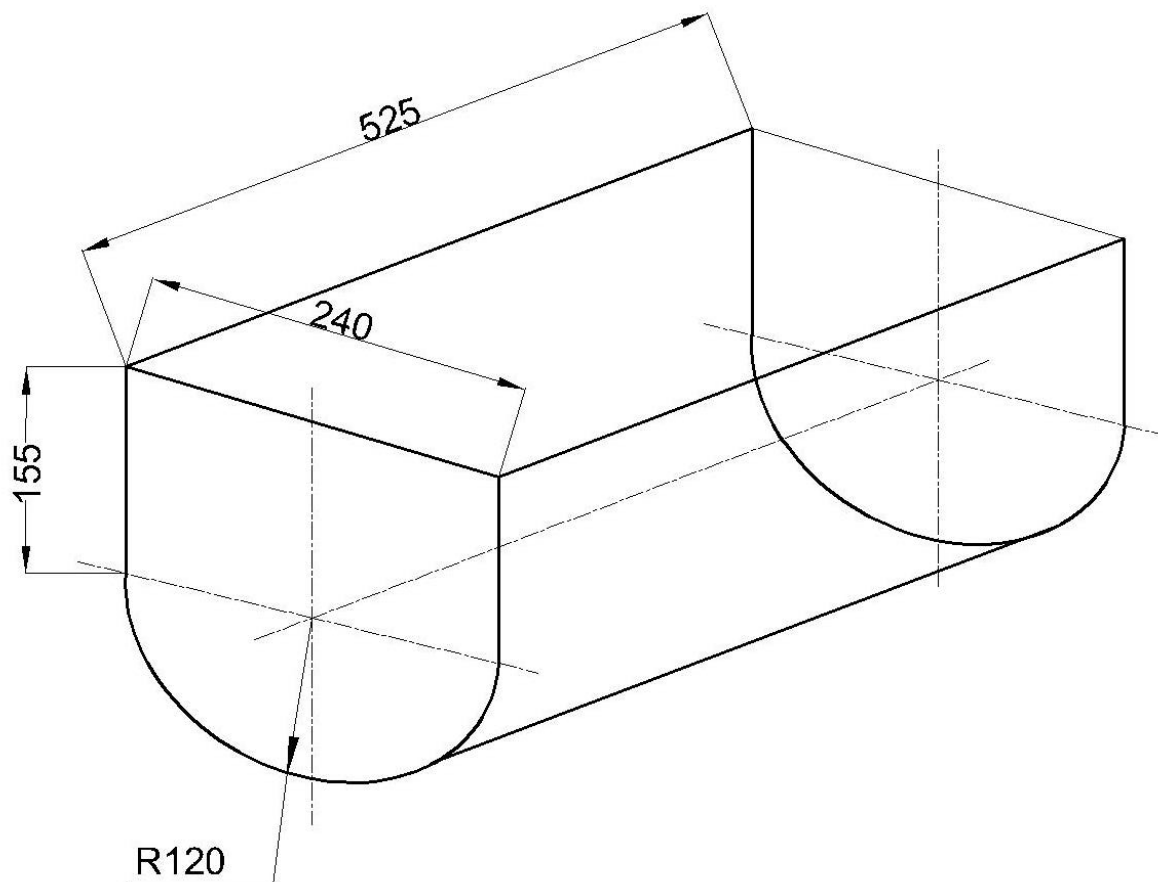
Розміри корпусу змішувача ЛН-24
